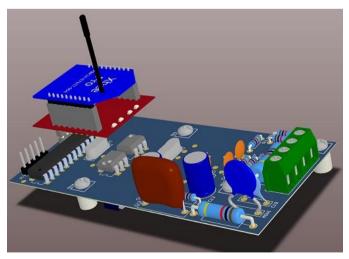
Rediseño del PCB del prototipo – Vista tridimensional.
